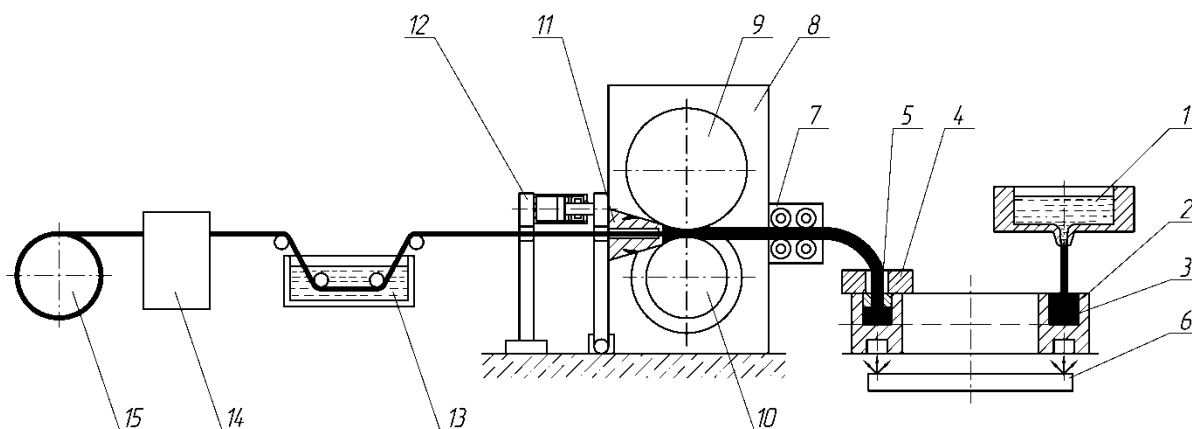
Схема установки для непрерывного литья, прокатки и прессования металла [94]:
